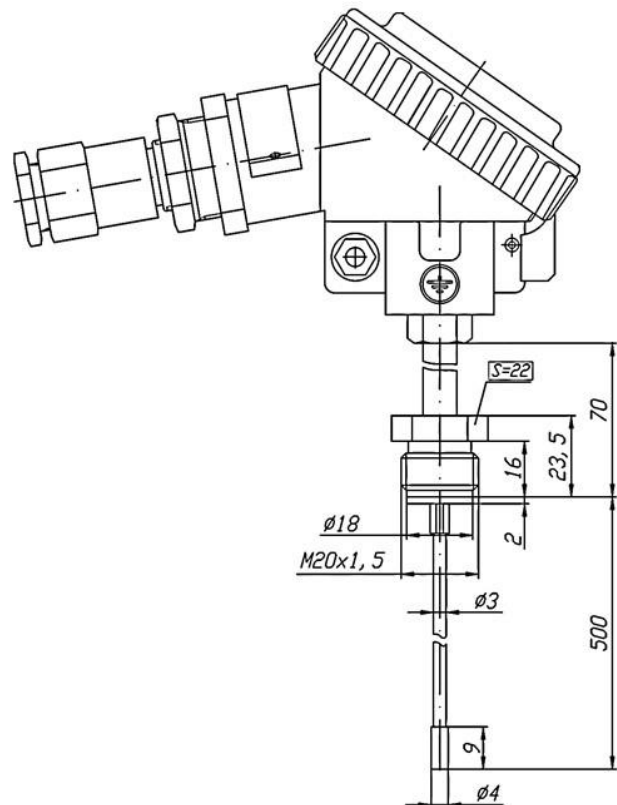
Чертеж установочного устройства РГАЖ 4.168.030-D.
